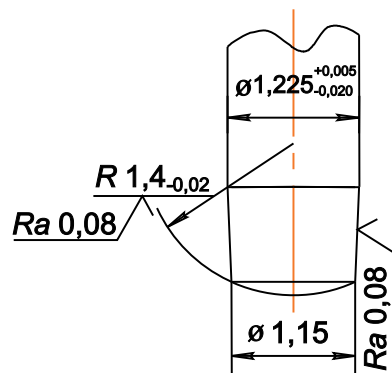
Эскиз опоры со сферической рабочей поверхностью
